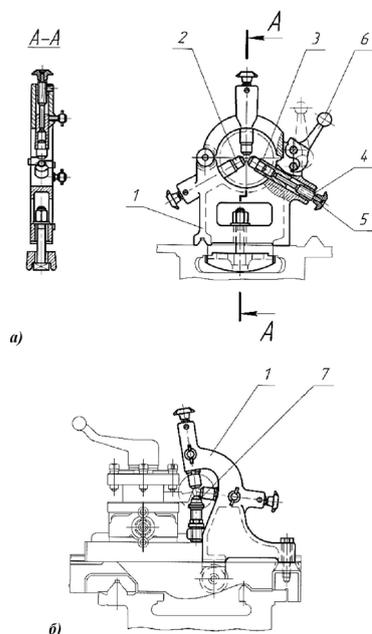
Типы токарных люнетов: а) неподвижный; б) подвижный.
